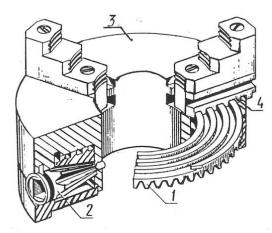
Самоцентрирующийся трехкулачковый патрон: 1 — диск; 2 — зубчатое колесо; 3 — корпус; 4 — зуб кулачка
